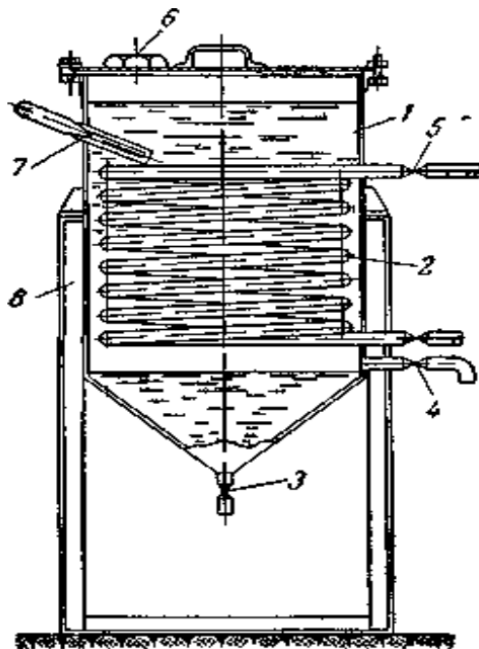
Схема типового відстійника з паровим підігрівом: 1 — корпус відстійника; 2 — паровий зміювик; 3 — спусковий кран; 4 — кран для виходу мастила; 5 — паровий вентиль; 6 — пробка для заливки мастила; 7 — кишень для термометра; 8 — каркас
